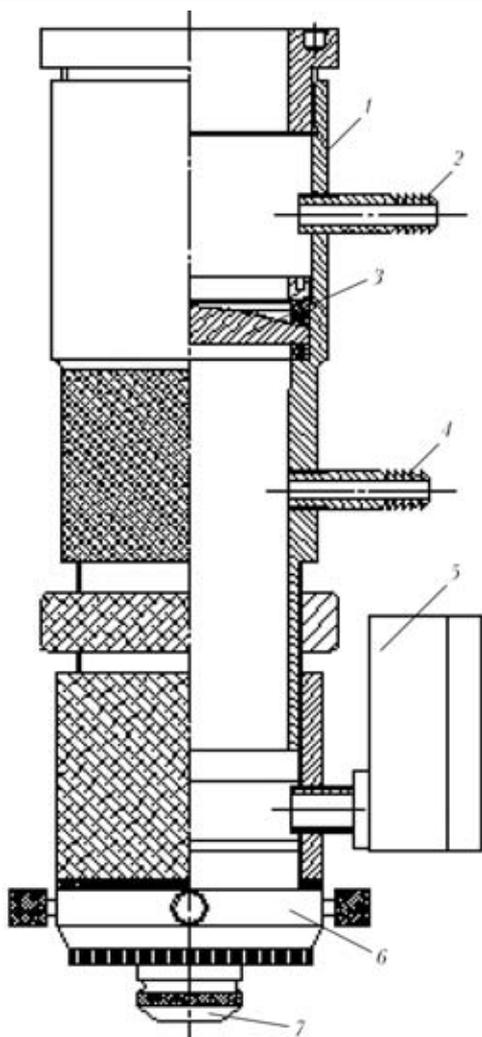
Схема лазерного резака, применяемого в технологическом комплексе для лазерной резки корпусов дисковых пил: 1 — корпус; 2 — штуцер воздушного охлаждения линзы; 3 — фокусирующая линза; 4 — штуцер для подачи режущего газа; 5 — манометр; 6 — система центровки режущего сопла; 7 — режущее сопло
